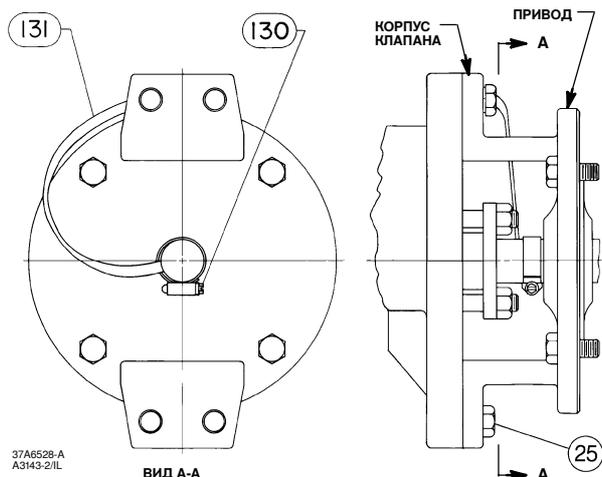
Дополнительный кабель заземления для замыкания вала на корпус
